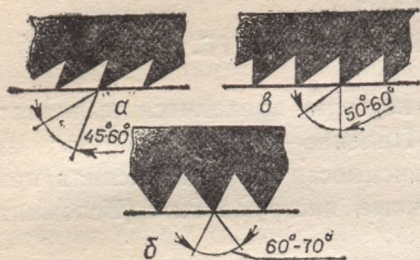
Форма и углы зубьев пил: α — для продольного пиления; β — для поперечного распиливания; γ — для смешанного пиления.
